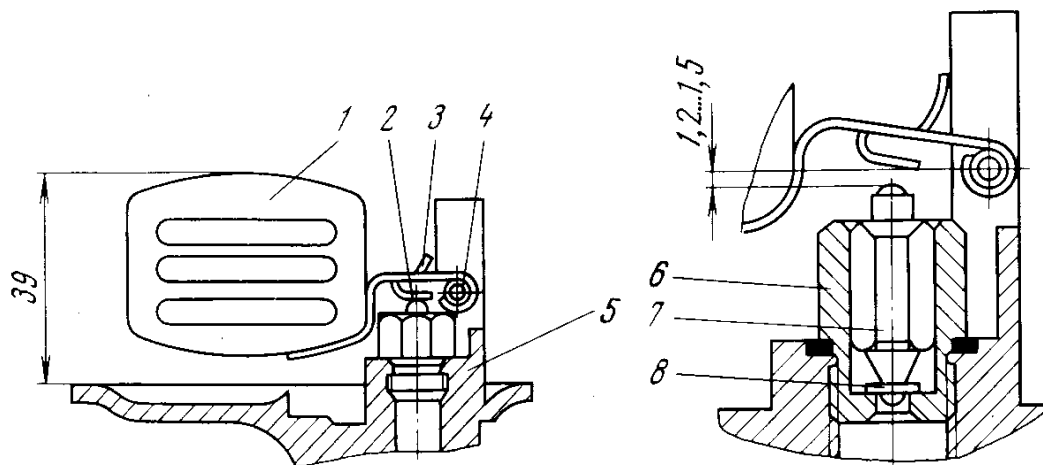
Поплавок с топливным клапаном: 1 — поплавок; 2 — язычок для установки уровня; 3 — ограничитель хода поплавка; 4 — ось поплавка; 5 — крышка поплавковой камеры; 6 — седло клапана подачи топлива; 7 — игла клапана подачи топлива; 8 — уплотнительная резиновая шайба
